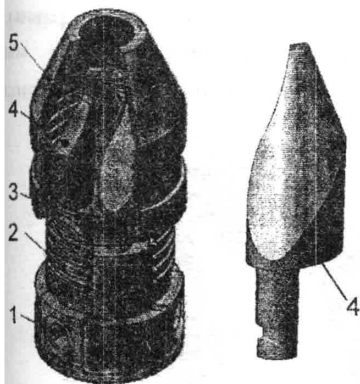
CAD-модель эксцентрикового сверлильно-фрезерного патрона: 1 – эксцентрик; 2 – резьбовая вставка; 3 – корпус; 4 – эксцентриковый кулачок; 5 – конусная втулка
